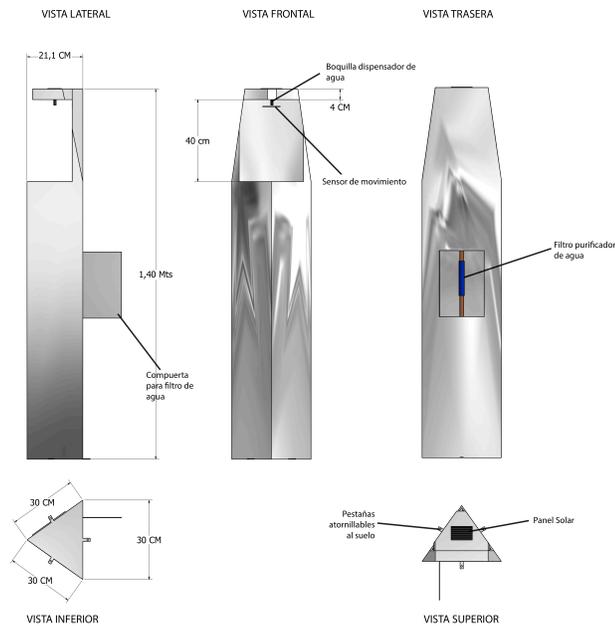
Planimetría del *render* dispensador de agua. Fuente: Elaboración propia
